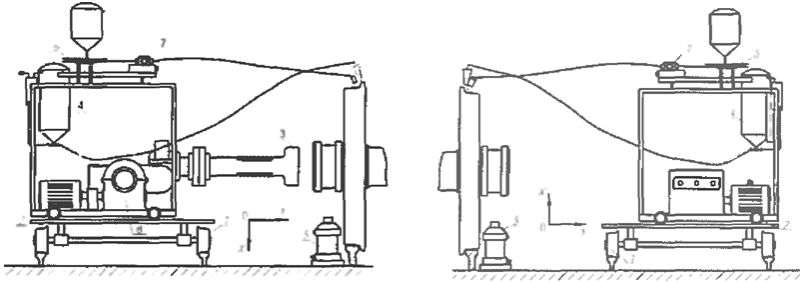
Установка для наплавлення гребенів колісних пар без викатки
